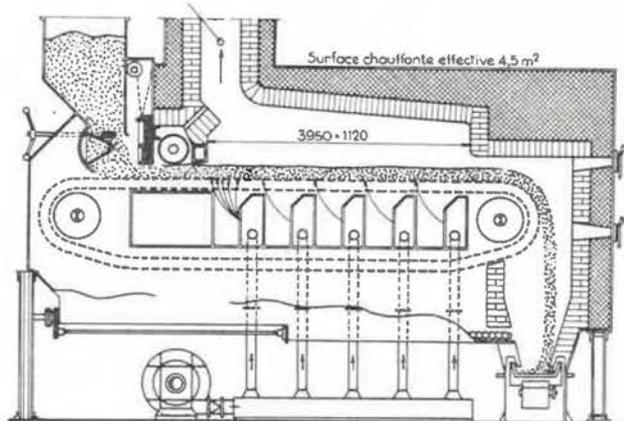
Unité à grille à poussée en dessous Baum-Steinmüller (d'après Andersen).
